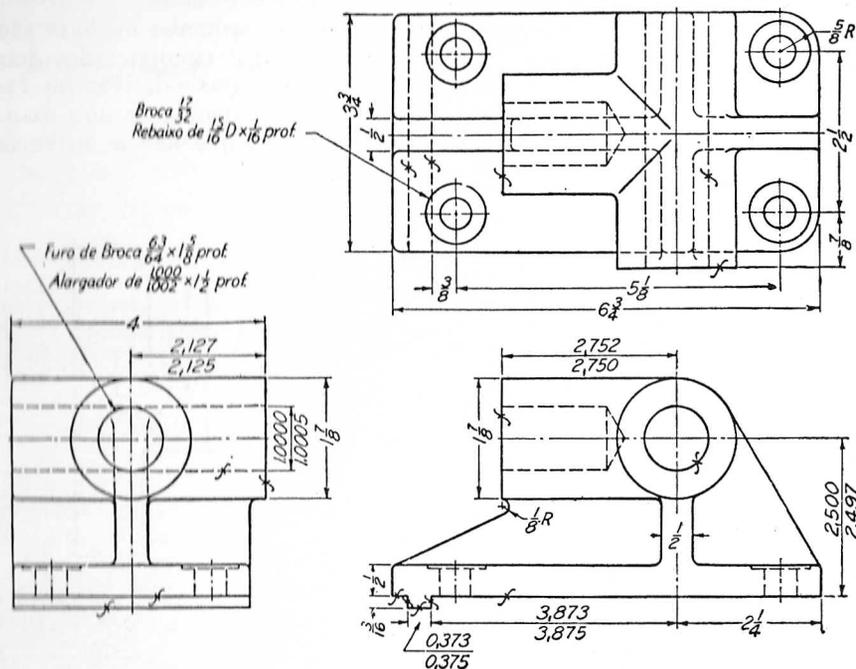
Exemplo de dimensionamento (suporte angular do eixo)
